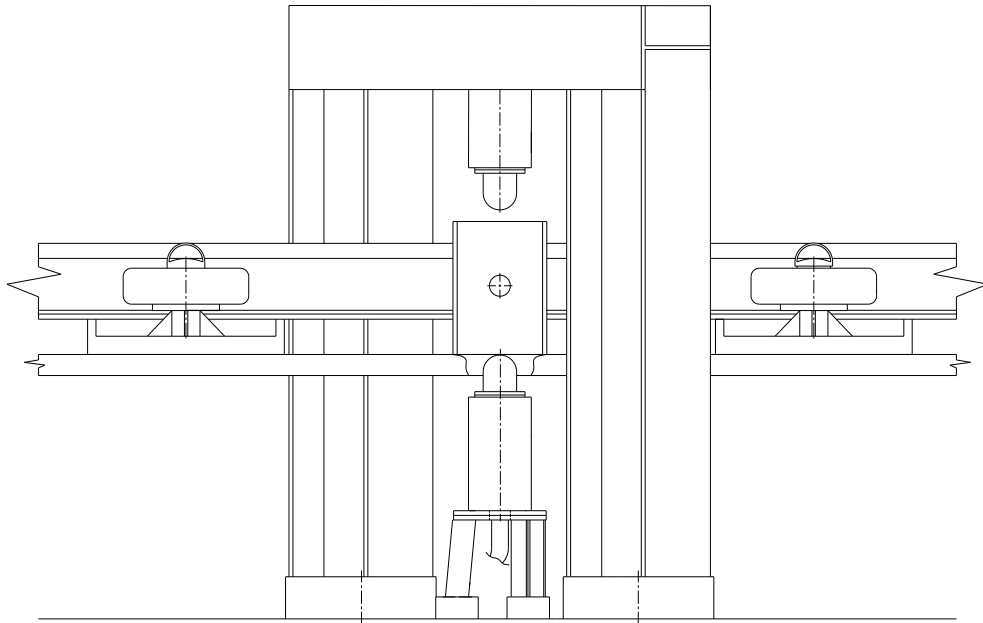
Принципиальная схема пресса горячей правки сварного стыка
